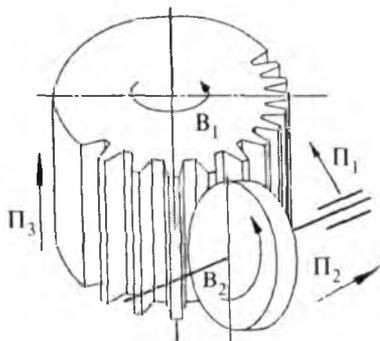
Нарезание зубчатых колес методом обкатки червячной фрезой
